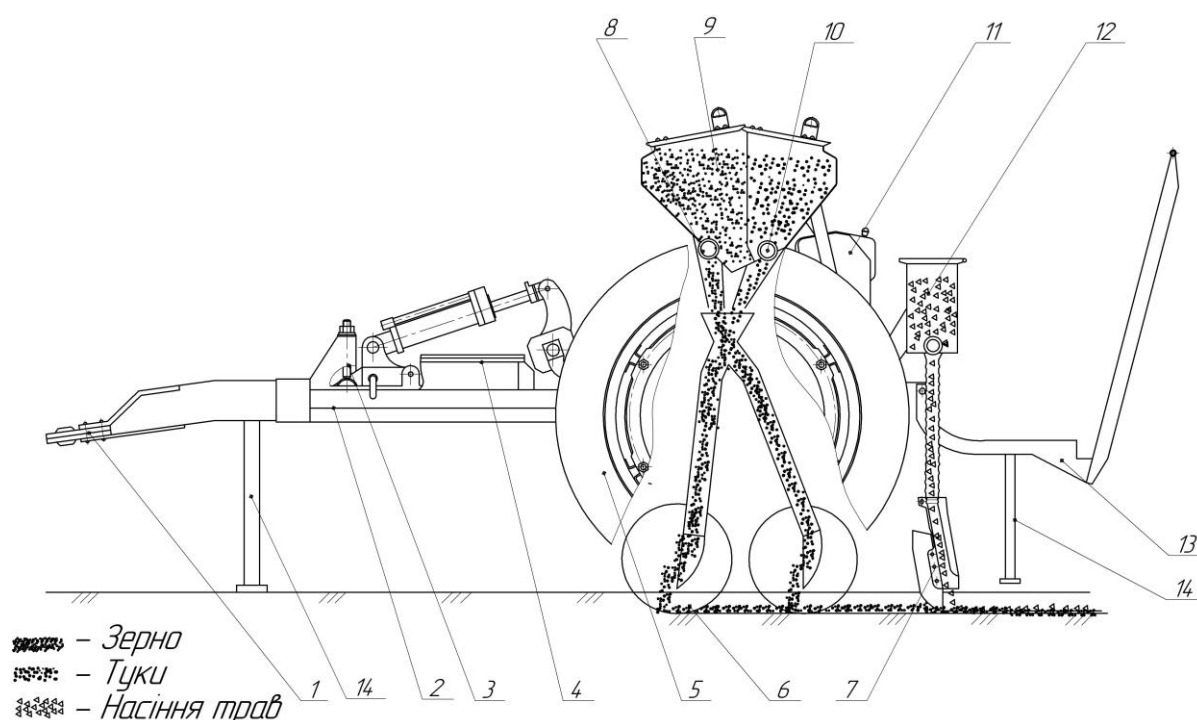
Загальний вигляд сівалки СЗТ-3,6: 1 – причіпний пристрій; 2 – рама; 3 – механізм регулювання глибини ходу сошників; 4 – інструментальний ящик; 5 – опорно-приводне колесо; 6 – зернотуковий сошник; 7 – трав'яний сошник; 8 – зерновий висівний апарат; 9 – зернотуковий ящик; 10 – туковисівний апарат; 11 – коробка передач; 12 – трав'яний ящик; 13 – підніжна дошка; 14 – підніжка
